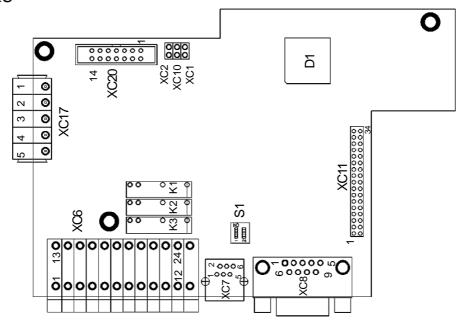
Cartão POS2 - destaque conectores e jumpers
